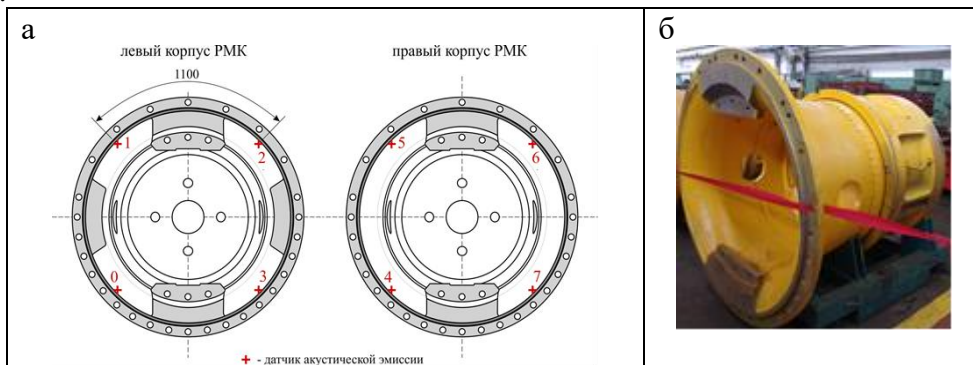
Схема расположения АЭ преобразователей (а); корпус РМК (б)
